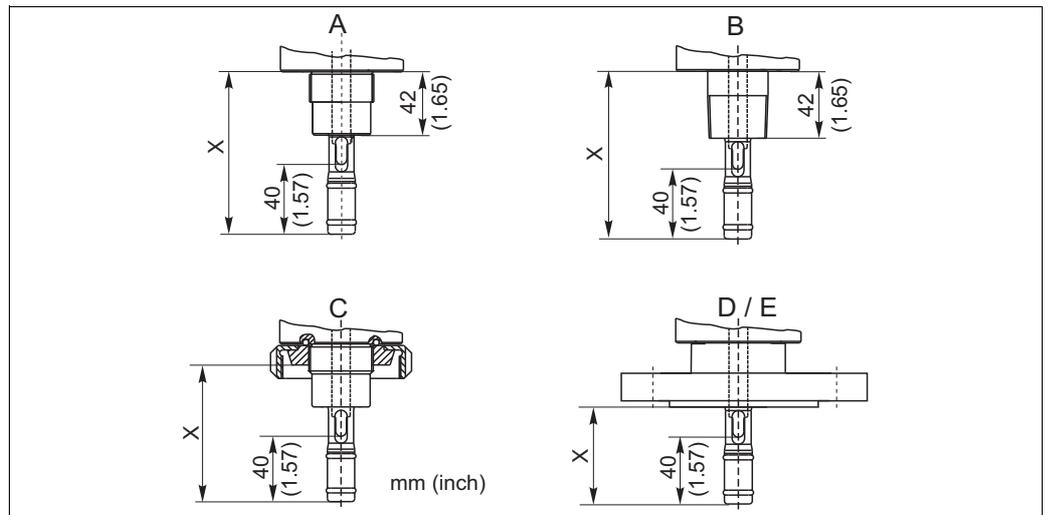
Prozessanschlüsse kurze Ausführung / lange Ausführung
